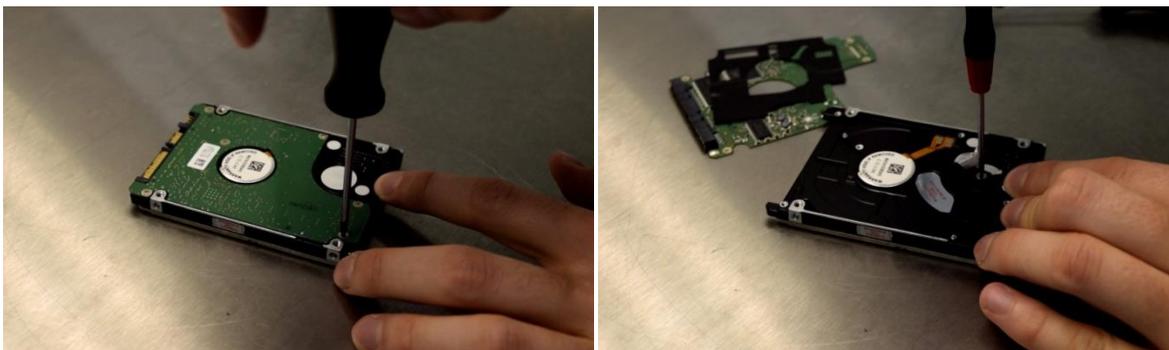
PCB の取り外しと底部からヘッドアセンブリを固定するネジを緩めて締める。
